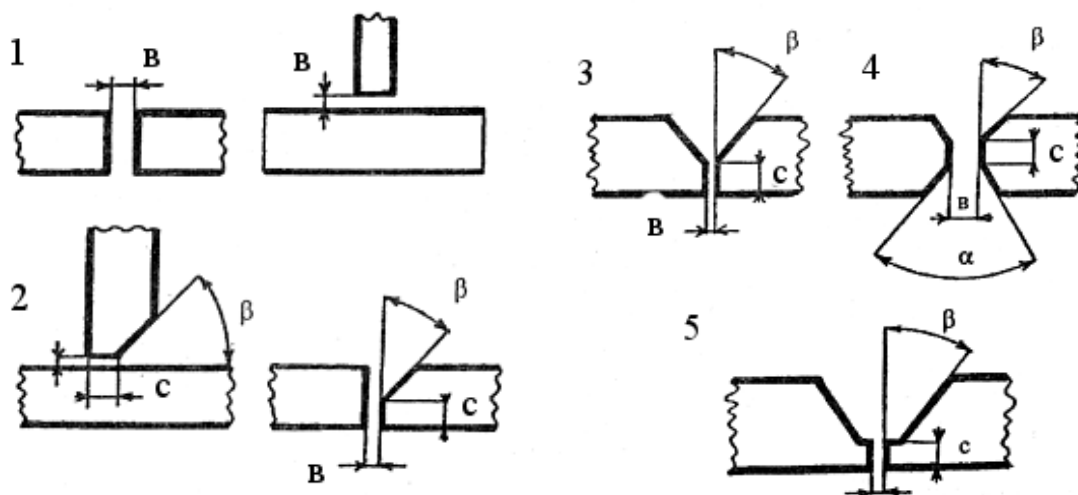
Параметры разделки кромок сварных соединений
